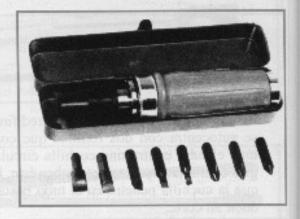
Destornillador de impacto y juego de puntas intercambiables.
